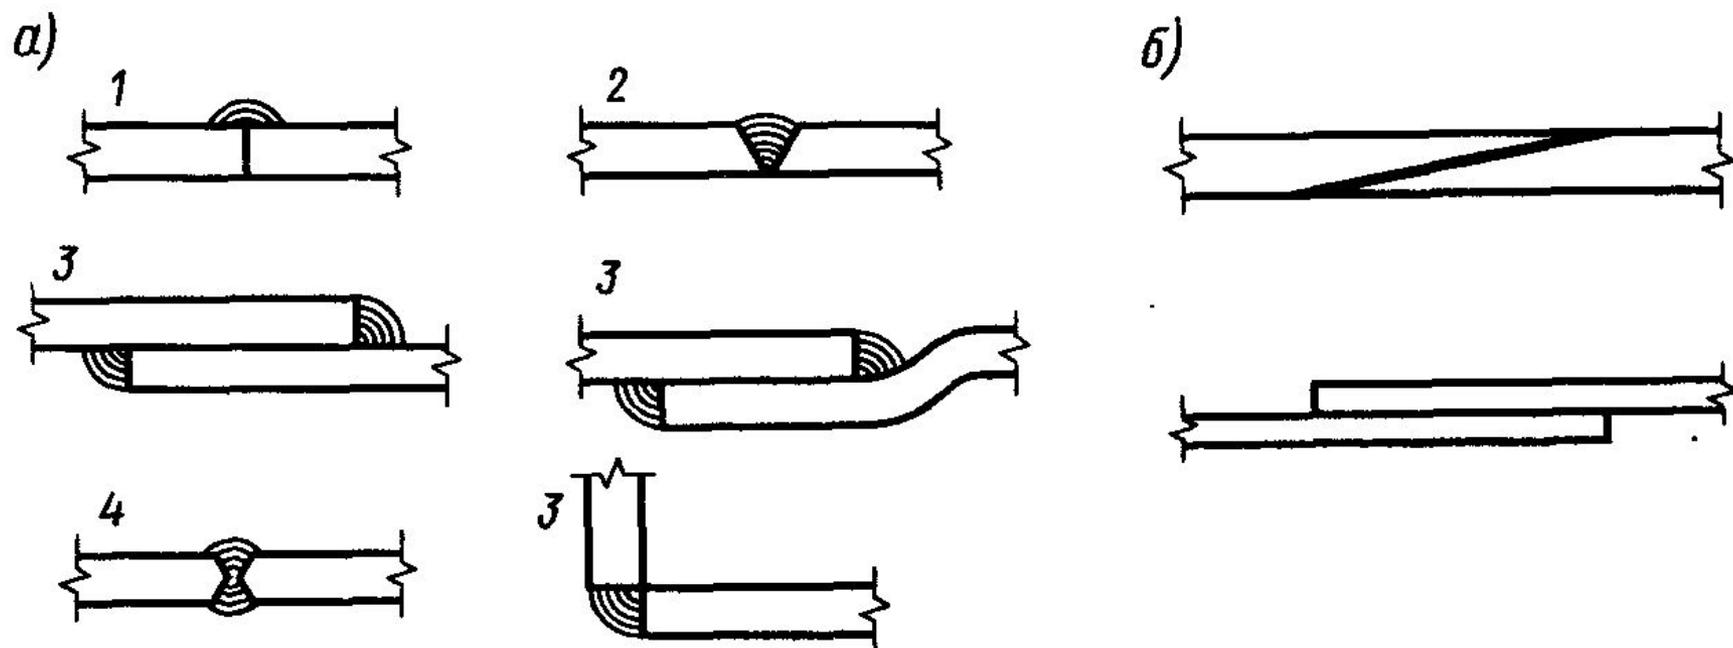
Сварные соединения термопластических пластмасс:
